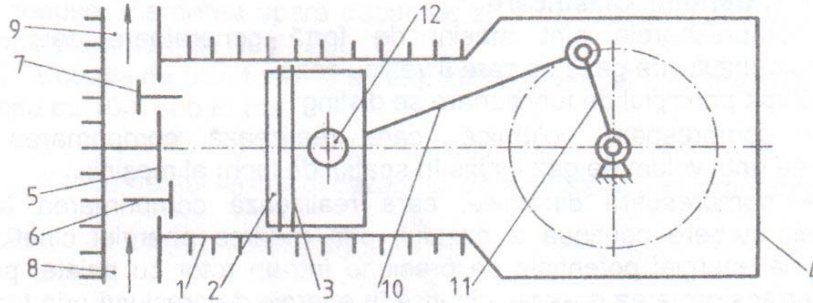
Schema constructivă a unui compresor cu piston:
